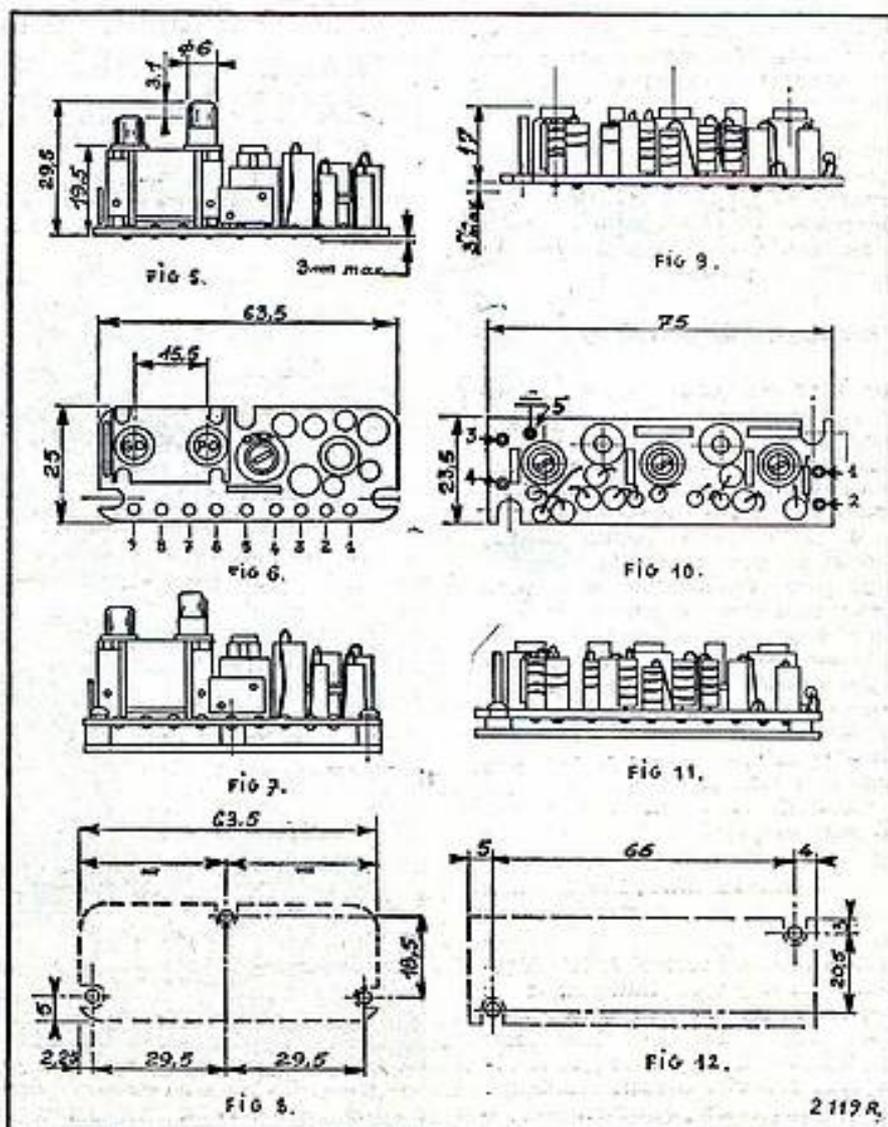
, 6, 7, 8 : module FW4B ; FIG. 9, 10, 11, 12 : module FB90. Disposition des pièces et encombrement.
